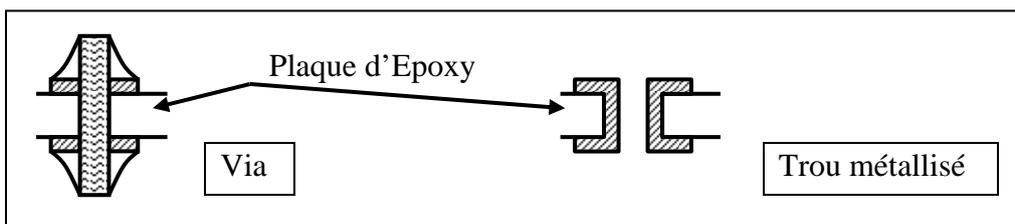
Vues en coupe d'une via et d'un trou métallisé.
